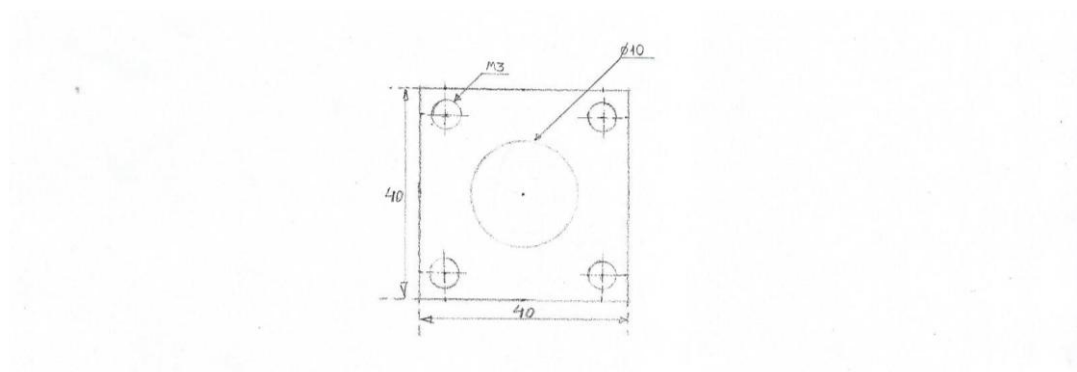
Tampa para o motor com eixo de 4 milímetros
